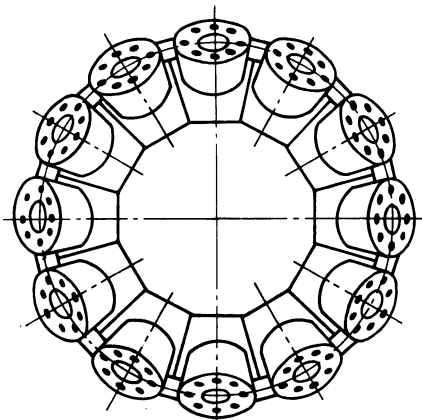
Круговое сопло: 1 – каналы для рабочих газов; 2 – канал для подачи порошка; 3 – корпус головки; 4 – накидная гайка (схематично); 5 – сопловой наконечник.
